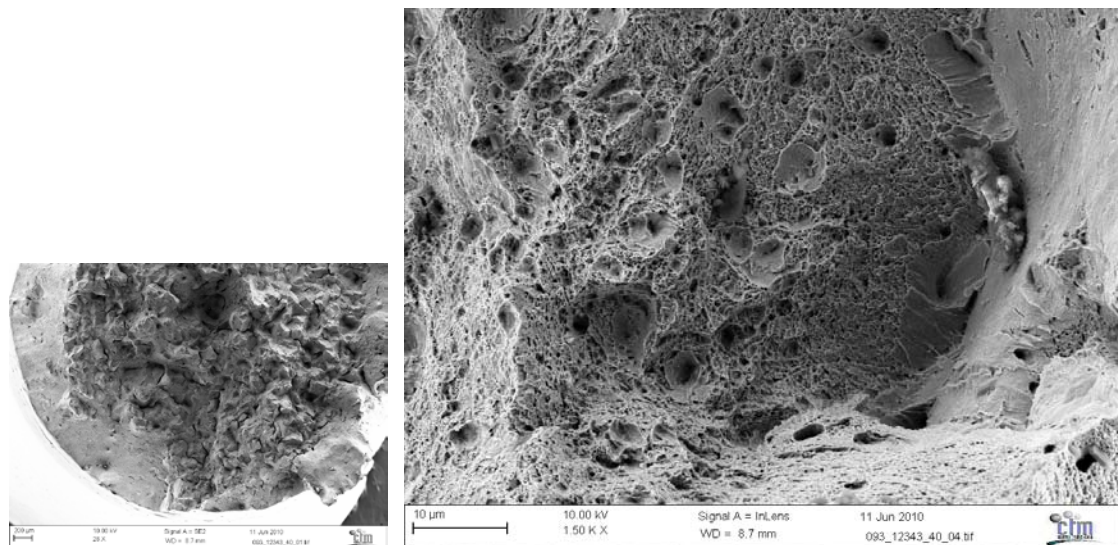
Superfície de fractura de la proveta de 1.2343 assajada en aire a 40°C.
